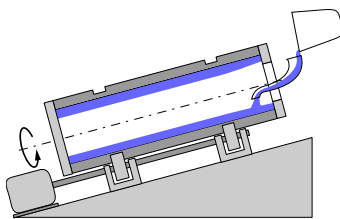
rfZ) Prinzip einer Schleudergussmaschine
